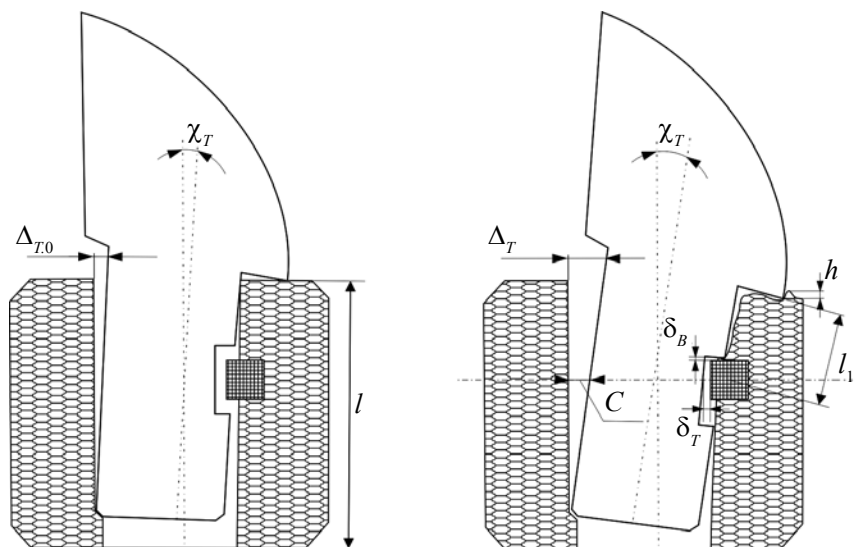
Пассивное закрепление резца в новом и изношенном резцедержателях
